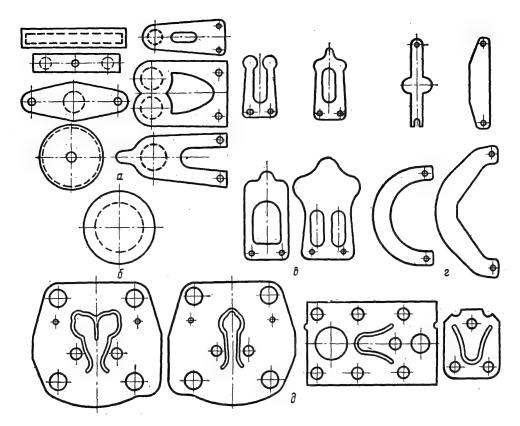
, Клапанные пластины малых герметичных компрессоров.
